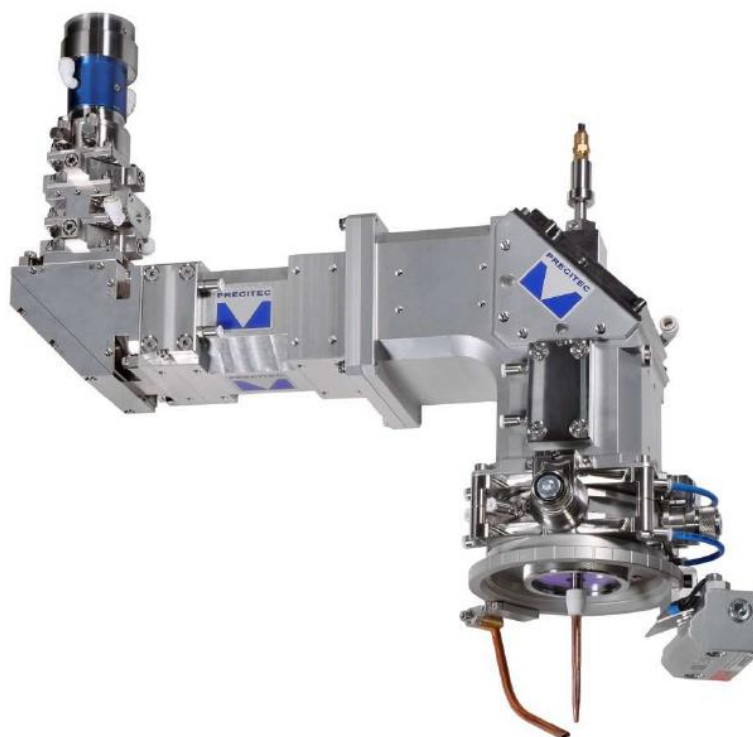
Lasermech, koaxiální hlava FiberWELD DH [54]
